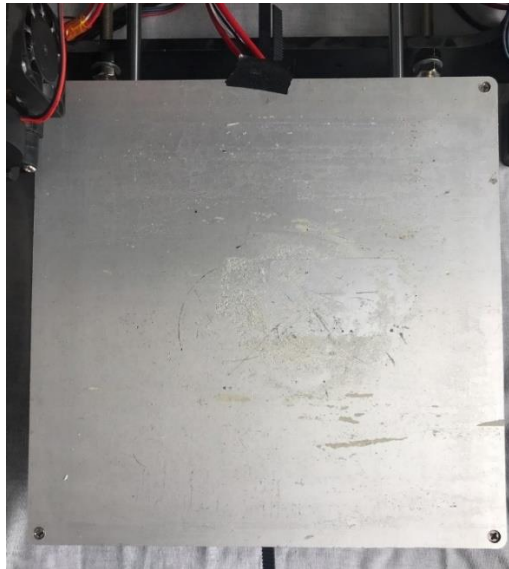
Parte superior de la cama de impresión hecha de aluminio
